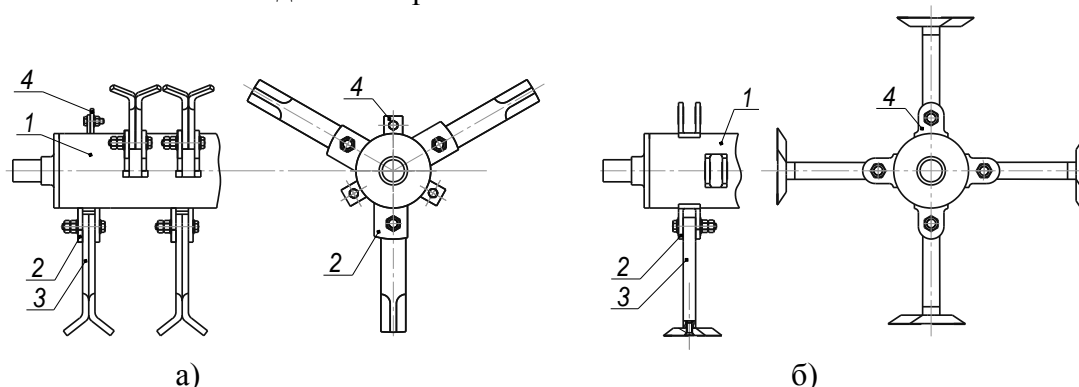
Загальний вигляд ротора мульчувача базової (а) та пропонованої (б) конструкції.
